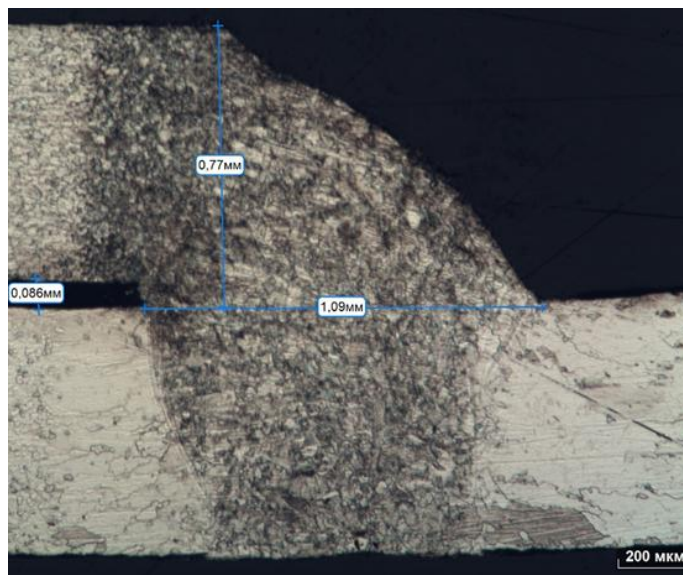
Лазерная сварка разнородных пластин внахлест (x50)
